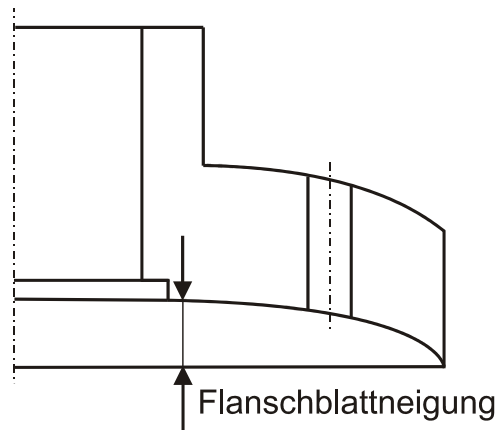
Messung der Flanschblattneigung bei Flansch B und C
